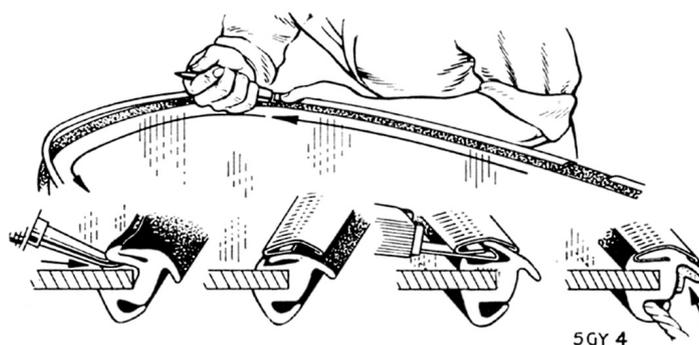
Montage de la moulure sur le pare-brise du coupé
